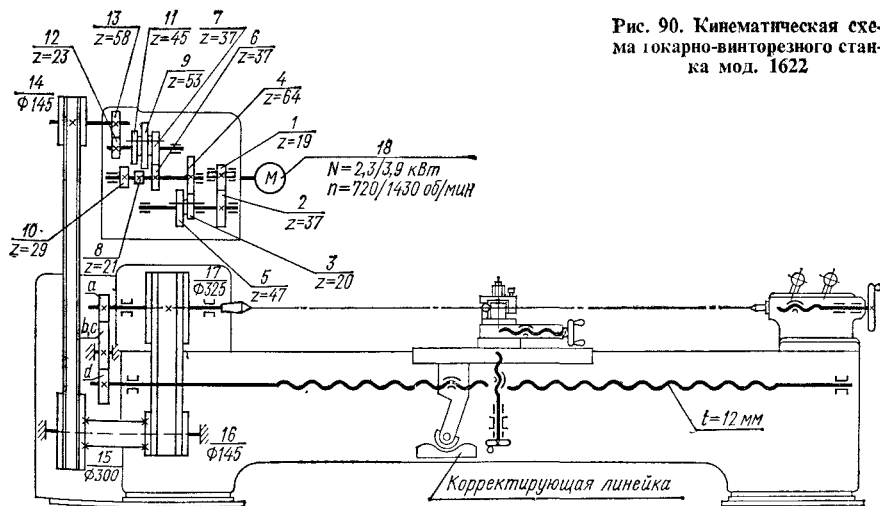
Кинематическая схема токарно-винторезного станка мод. 1622
